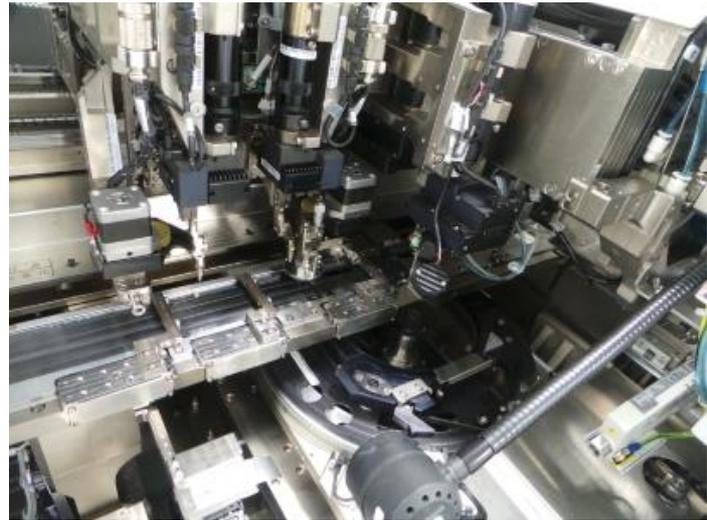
Фотографии установки AD830 монтажа чипов в корпус
